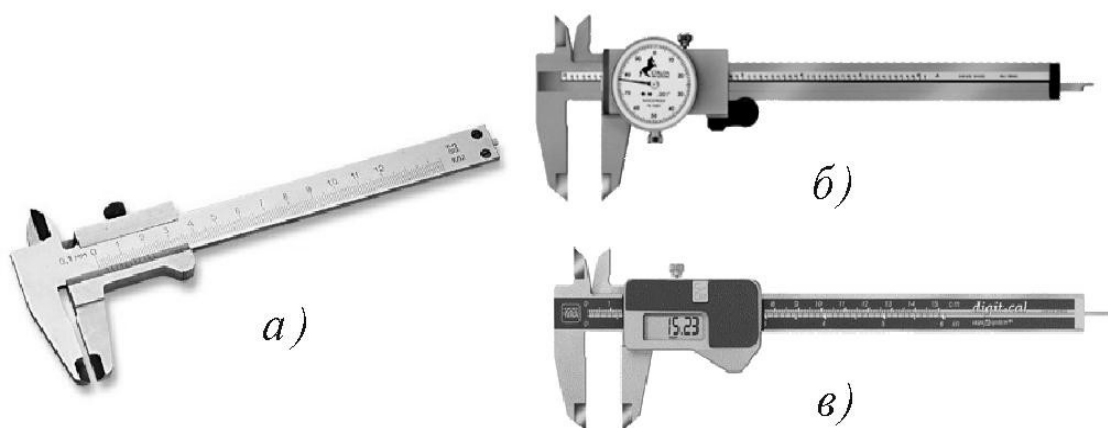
Модели штангенциркулей: а) нониусный; б) индикаторный; в) цифровой
